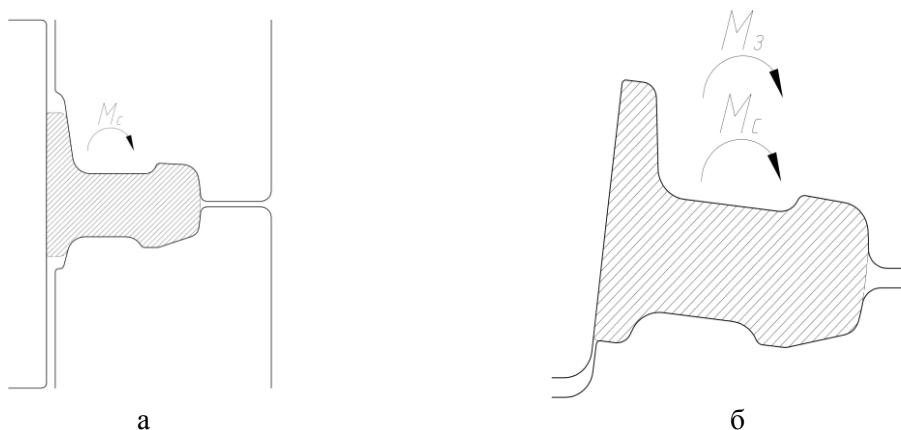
Общий вид универсального трехвалкового (а) и чистового двухвалкового (б) калибров для прокатки рельсов остряковых
